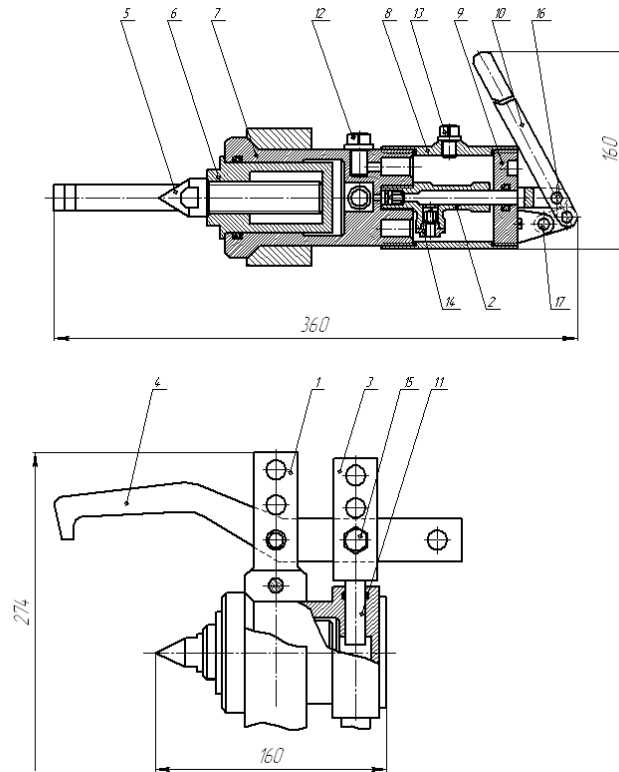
Універсальний гідравлічний знімач з вбудованим насосом: 1 - захват; 2 - траверса; 3 - болт; 4 - скоба; 5 - поршень; 6 - поршень; 7 - гвинт; 8 - корпус; 9 - насос; 10 - масляний резервуар; 11 - рукоятка; 12 - пробка; 13 - гвинт.
